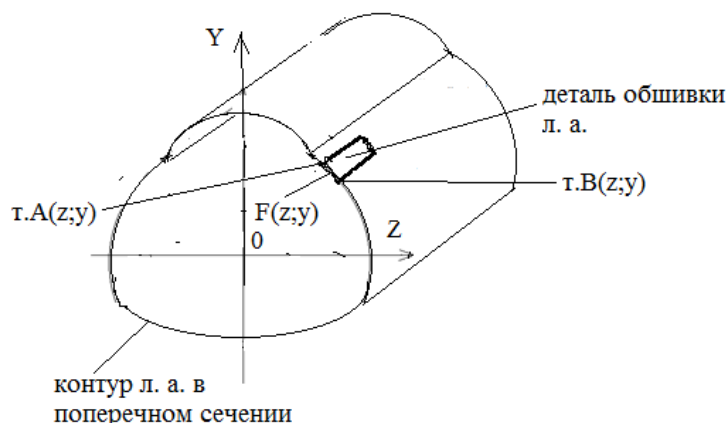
Схема расположения детали обшивки ЛА в декартовой системе координат Z0Y
